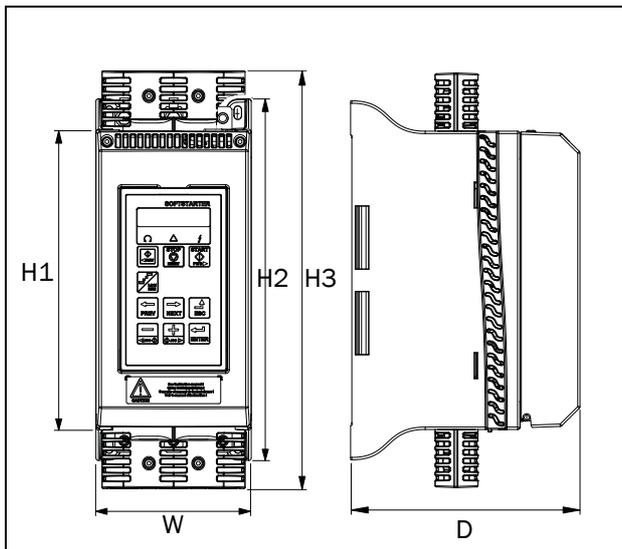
Dimensions des formats de châssis 1 et 2 du TSA
